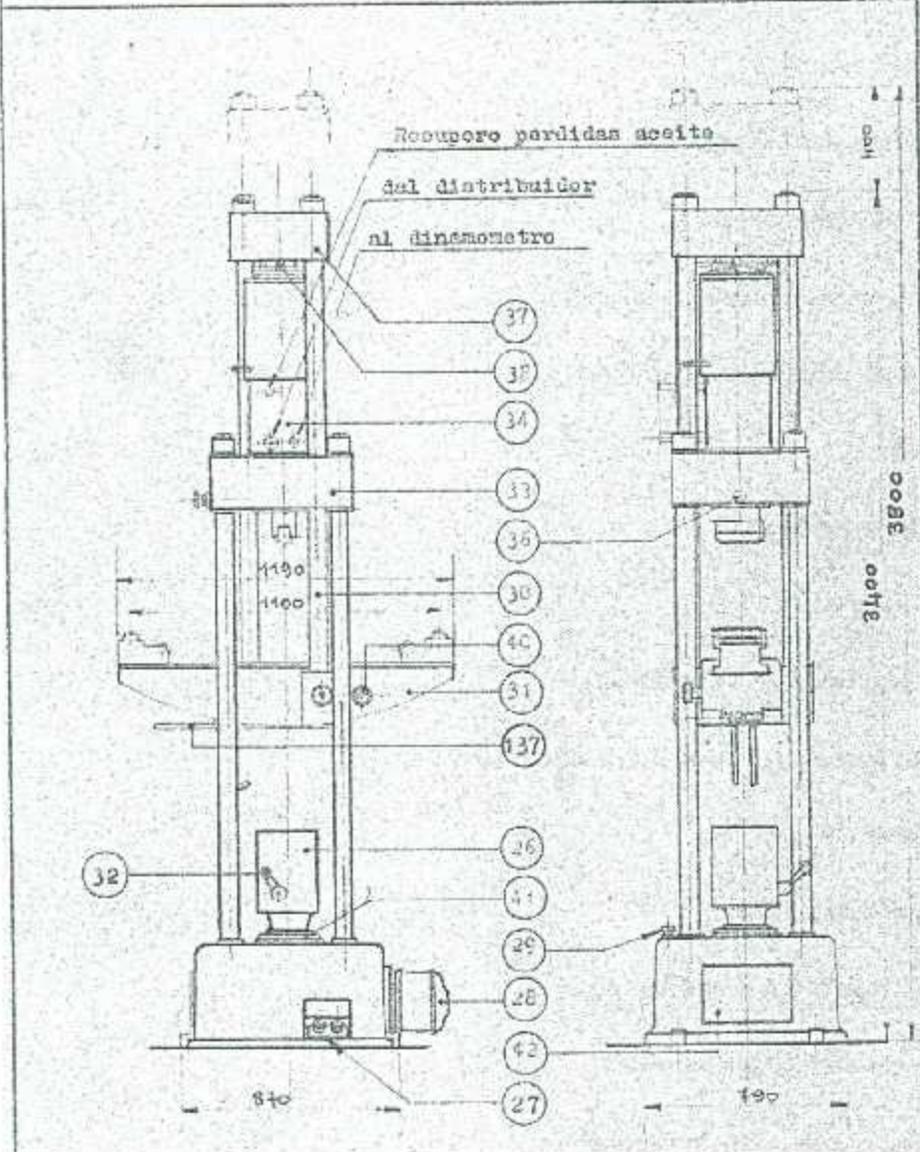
Vista isométrica de la máquina de ensayos universal, folio nº 15 -dibujo nº 517501/B
